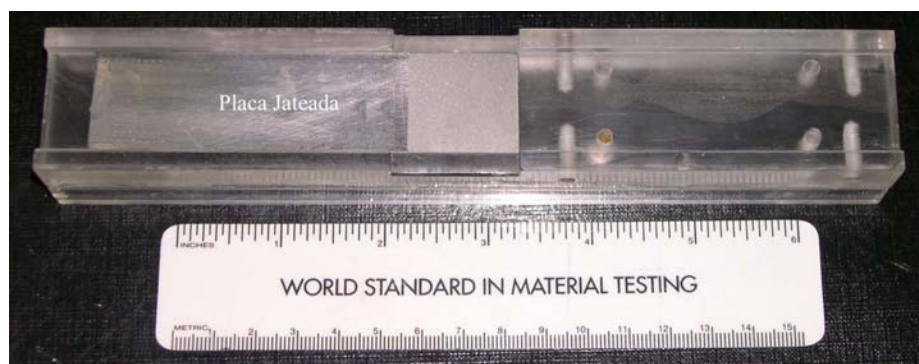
Primeiro Dispositivo de Colagem com as Placas Aderentes.
